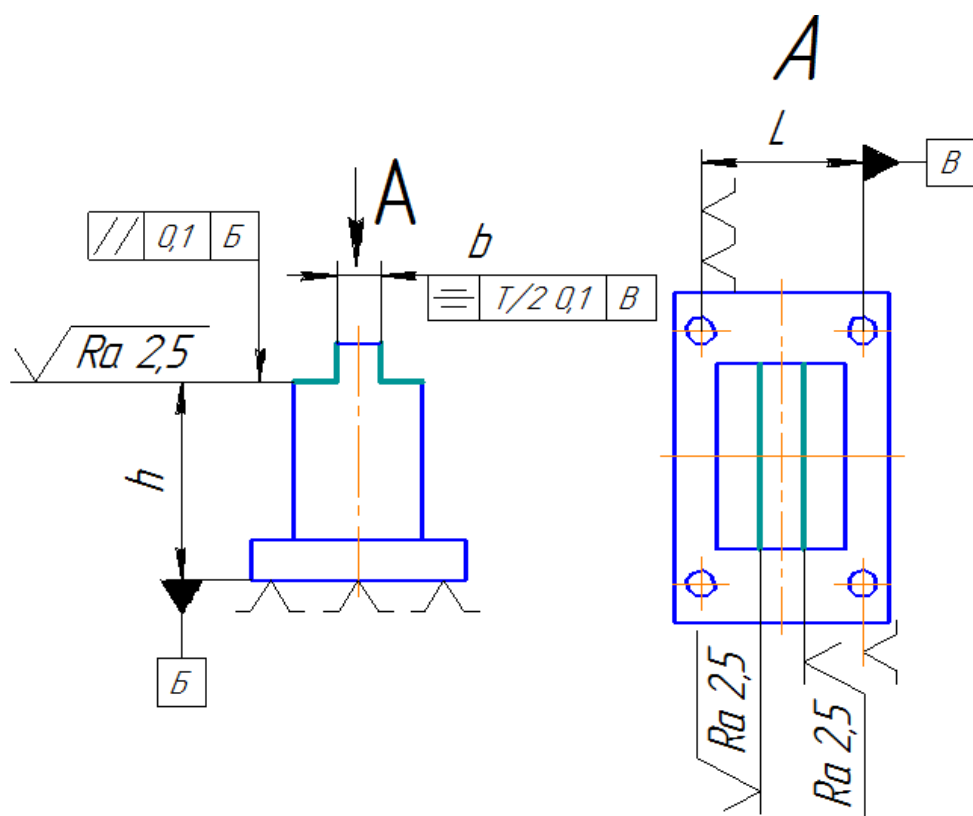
Чертеж обрабатываемой заготовки на консольно-фрезерном станке
